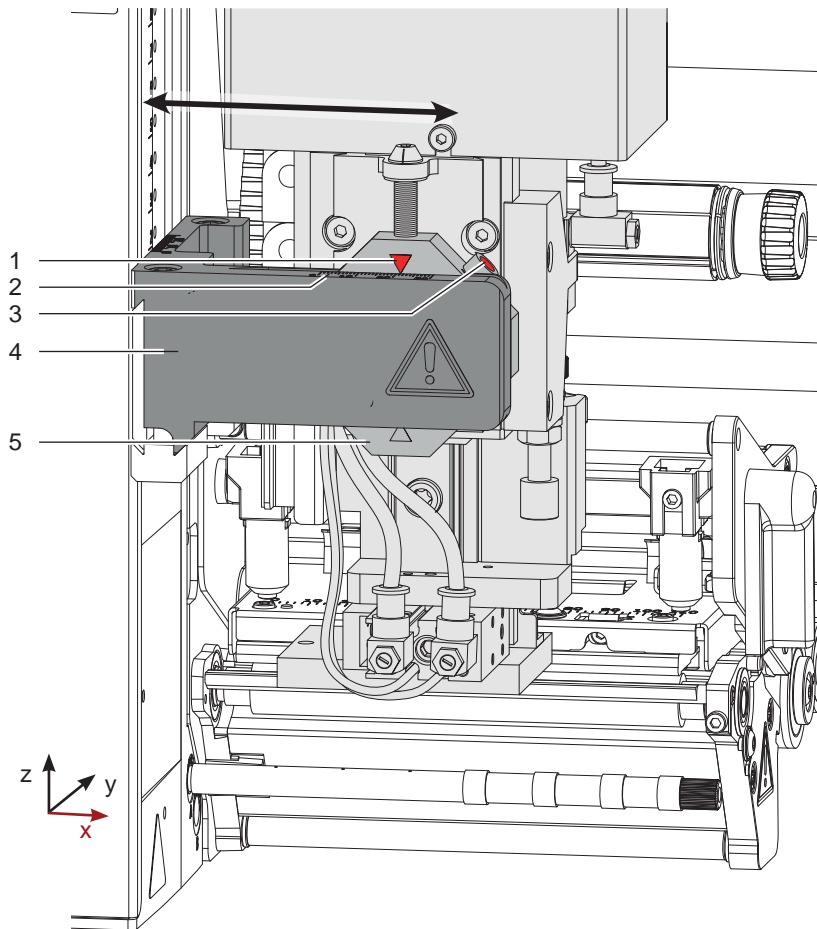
Verschiebung der Stempelbaugruppe in X-Richtung
